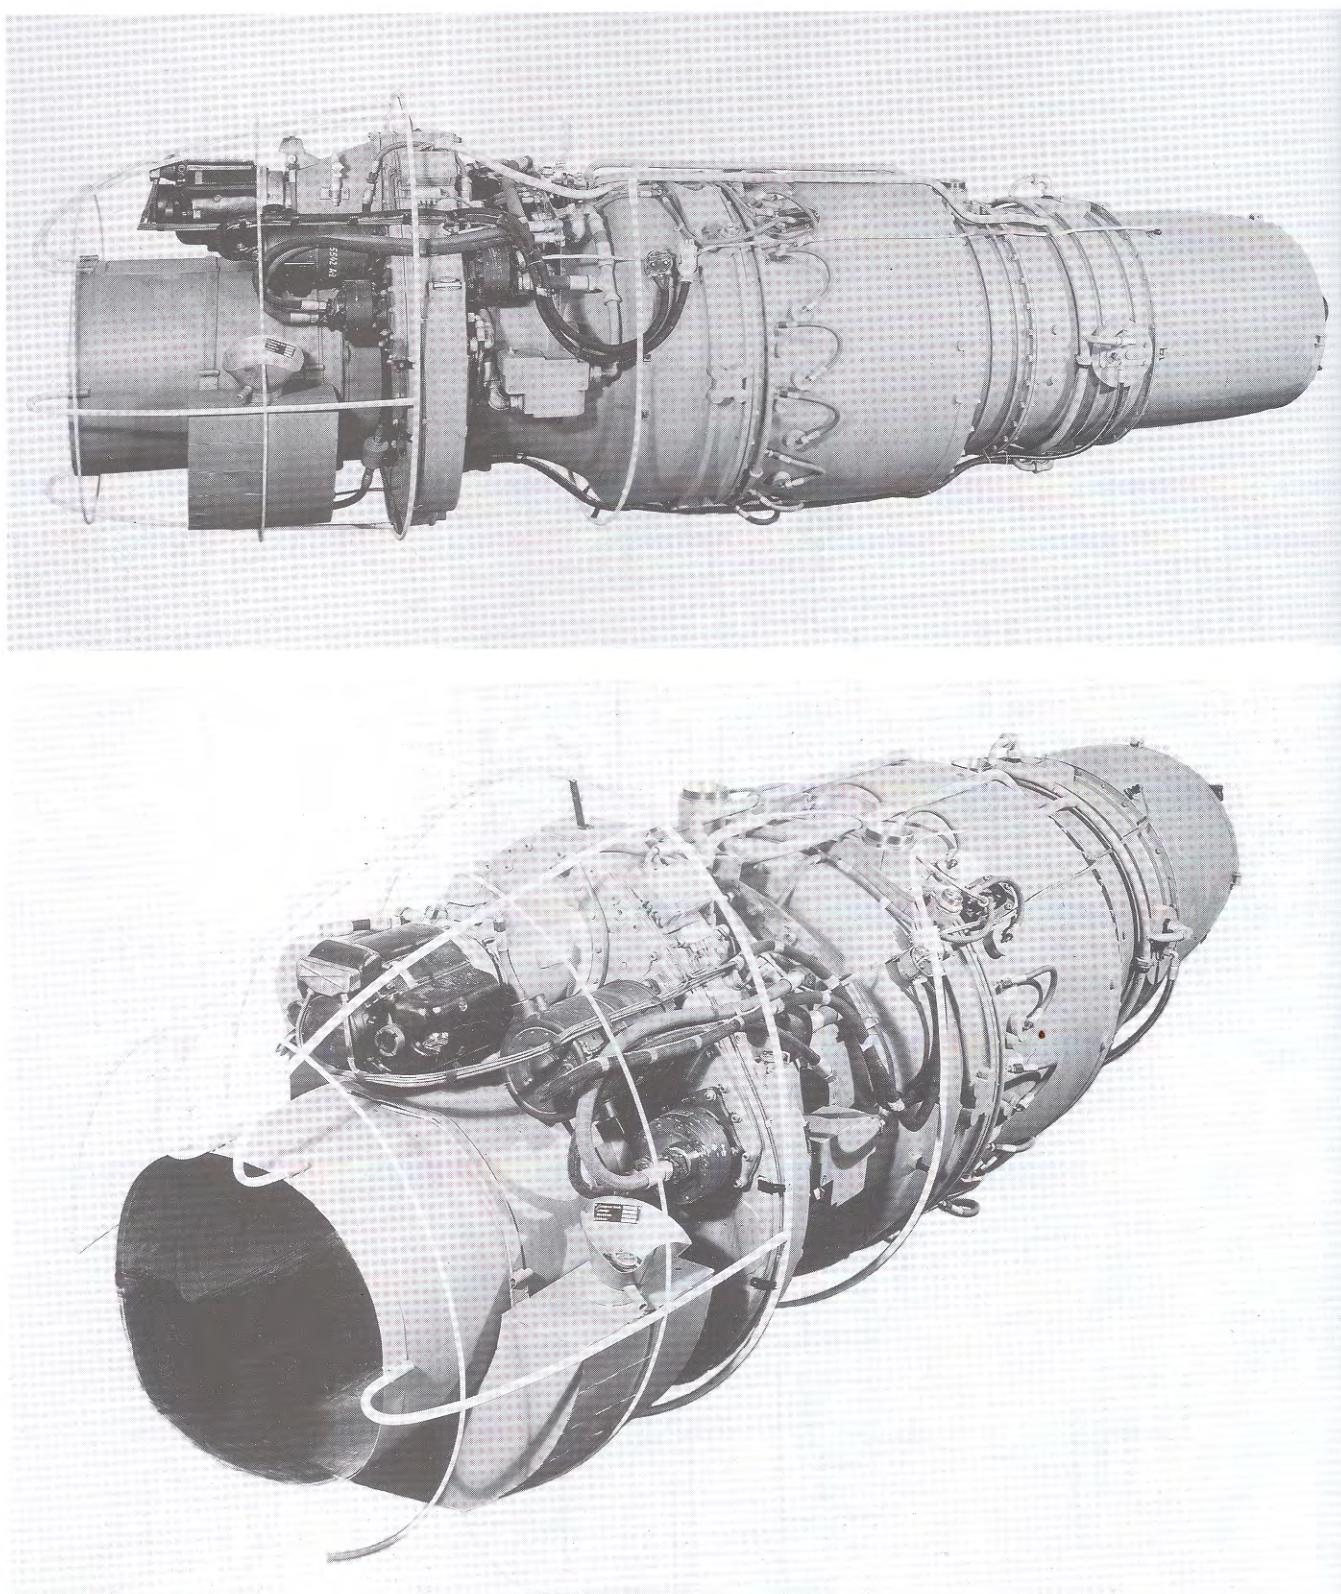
Макет турбореактивного двигателя Хейнкель-Хирт 109-011 А-0, изготовленный на этапе подготовки к производству. На макете установлен трубчатый каркас для проверки зазоров обтекателя. Хотя этот двигатель не был разработан полностью, тем не менее, к концу войны он стал одним из самых мощных двигателей в Германии (фотография сделана 14 марта 1945 года)
